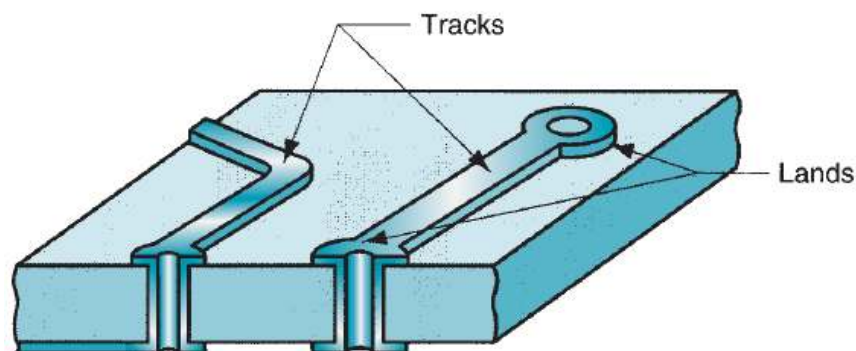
Esquema representativo da superfície da placa de circuito impresso [7].
